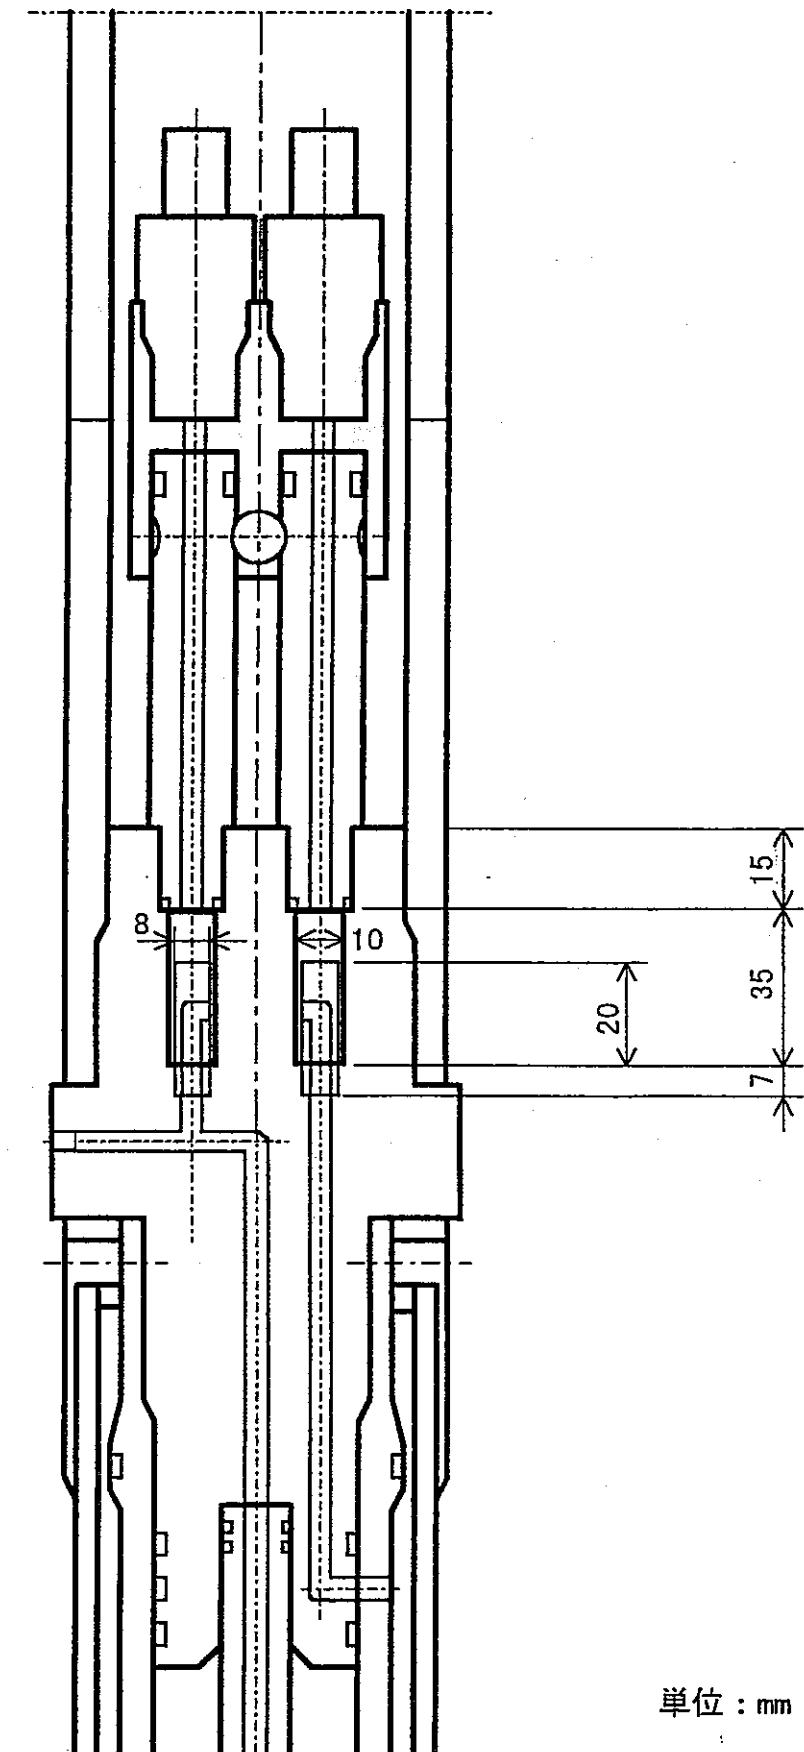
上部パッカ一部ラインフィルター設置状況図
